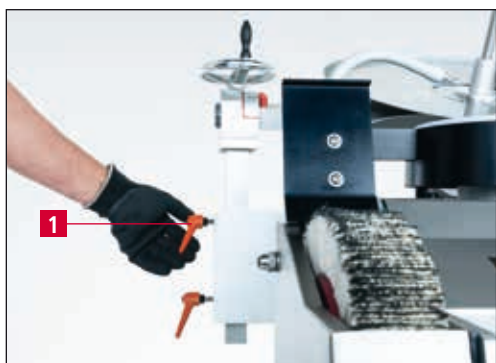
Настройка приспособления для заточки дисковых ножей
